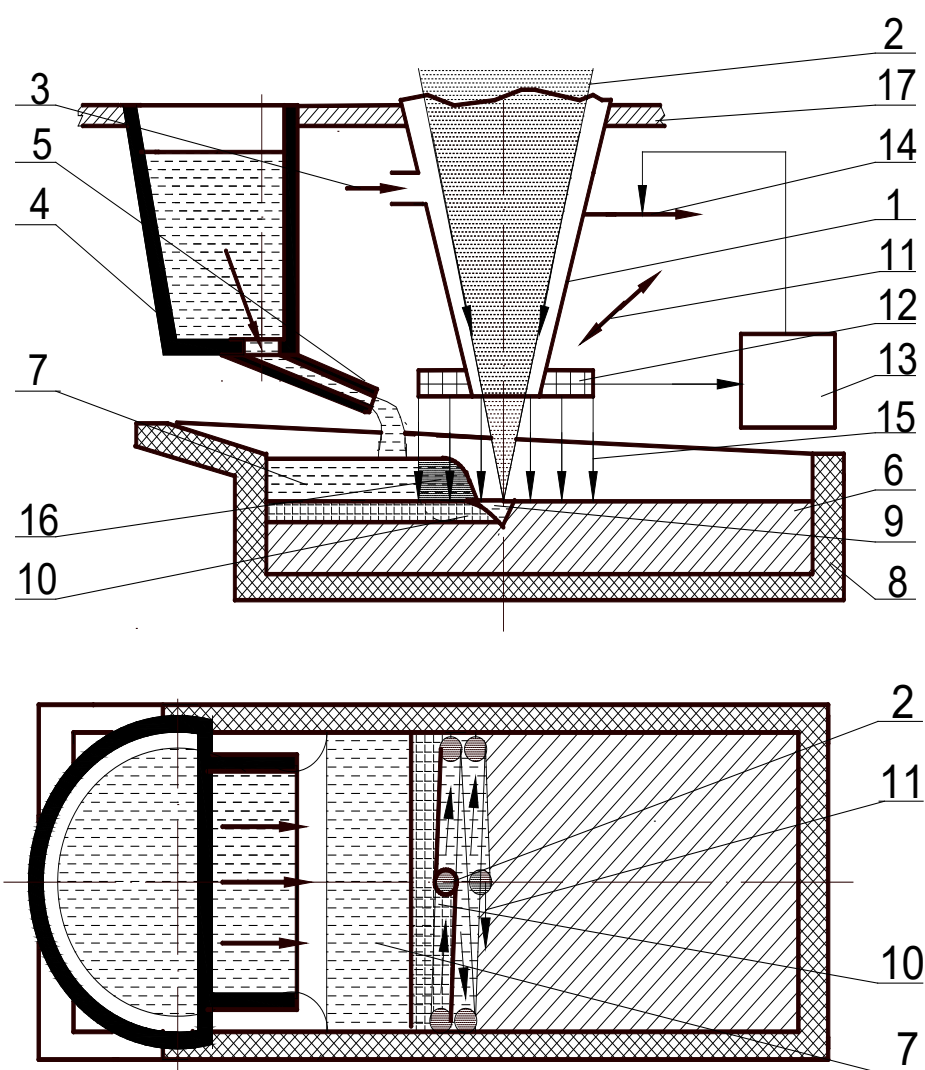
Пристрій для автоматизованого лазерно-ливарного виготовлення біметалів
